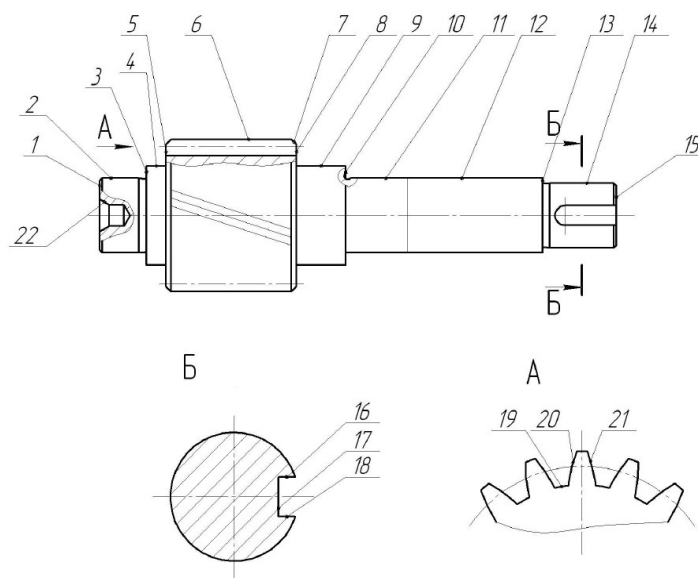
Вал-шестерня редуктора SZ 121 (позначення поверхонь)
